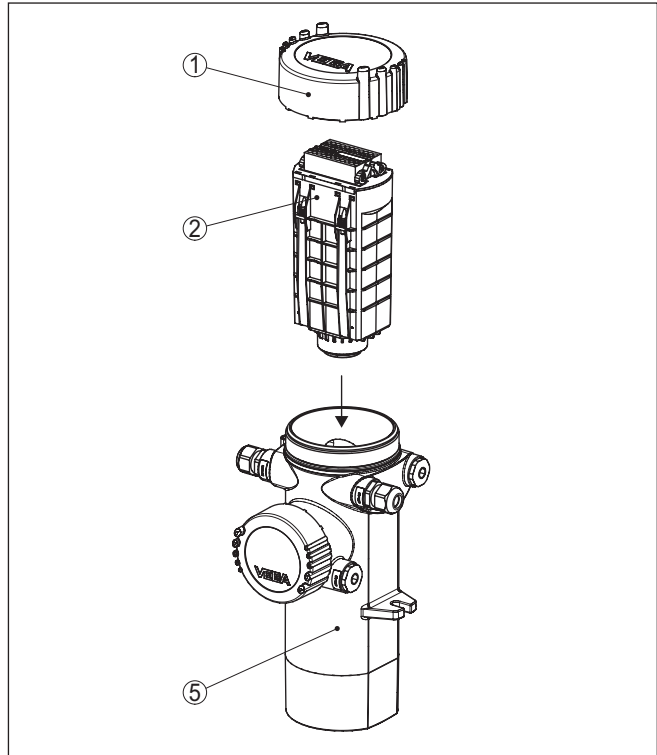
Elektronikereinsatz vorsichtig in das Gerätegehäuse einstecken
